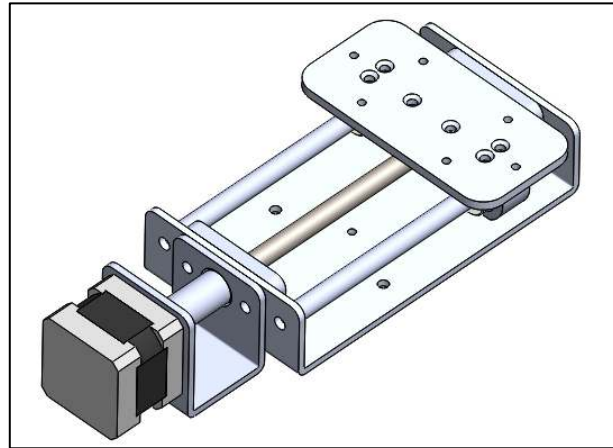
X, Y eksenleri ve taşıyıcı gövdesi montajı.
